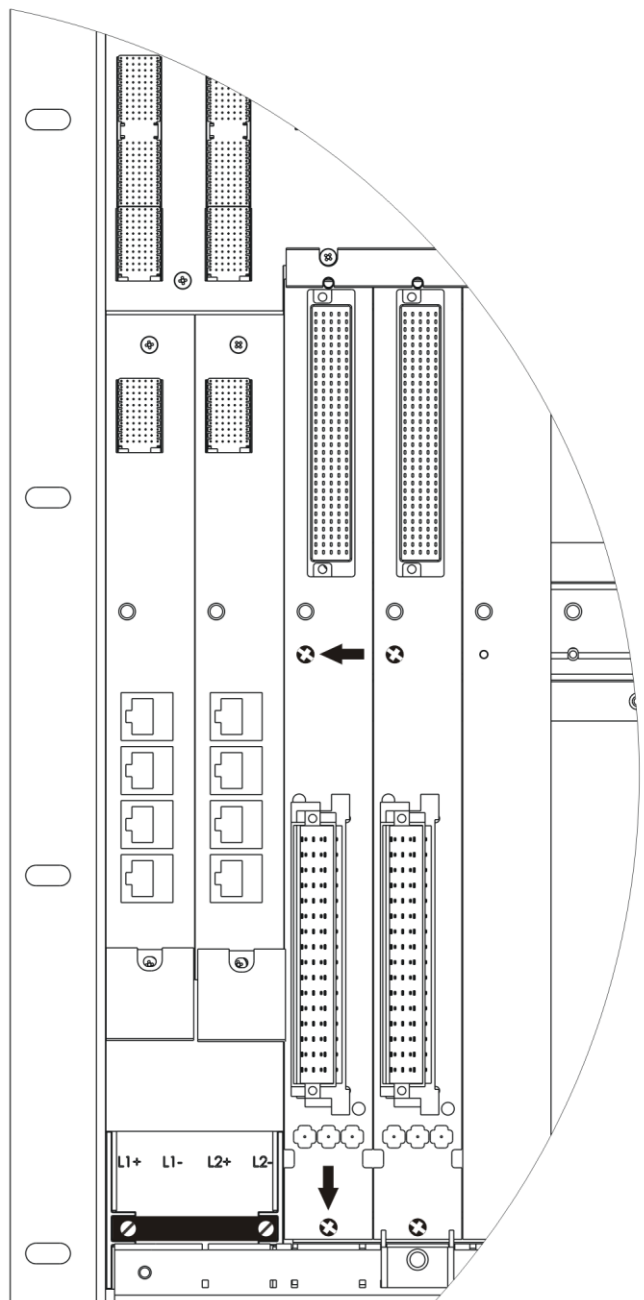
Exemple de fixation par vissage du panneau de raccordement mono
